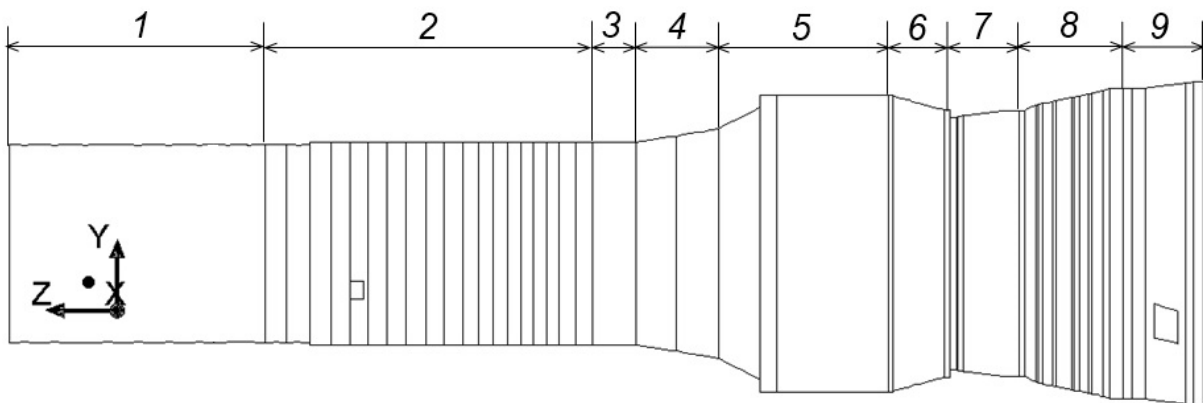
Характерные участки корпуса ГТД: 1 – проставка; 2 – корпус КНД; 3 – переходник; 4 – корпус силовой КВД; 5 – кожух камеры сгорания (КС); 6 – корпус силовой турбины высокого давления (ТВД) и турбины низкого давления (ТНД); 7 – опорный венец (ОВ) ТНД; 8 – корпус ТС; 9 – ОВ ТС
